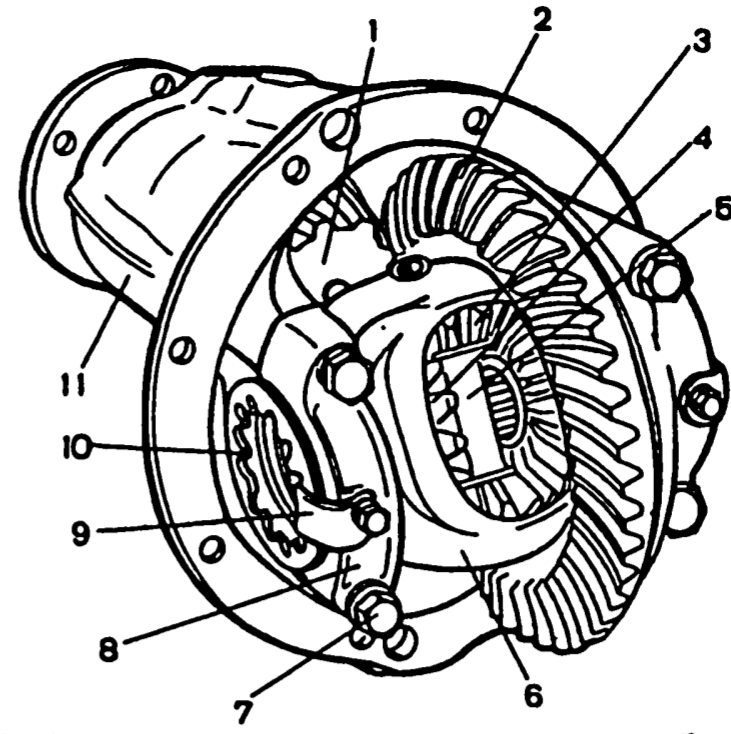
Редуктор заднего моста в сборе: 1 - ведущая шестерня; 2 - ведомая шестерня; 3 - сателлит; 4 - шестерня полуоси; 5 - ось сателлитов; 6 - коробка дифференциала; 7 - болты крепления крышки подшипника коробки дифференциала; 8 - крышка подшипника коробки дифференциала; 9 - пластина стопорная; 10 - регулировочная гайка подшипника; 11 - картер редуктора
